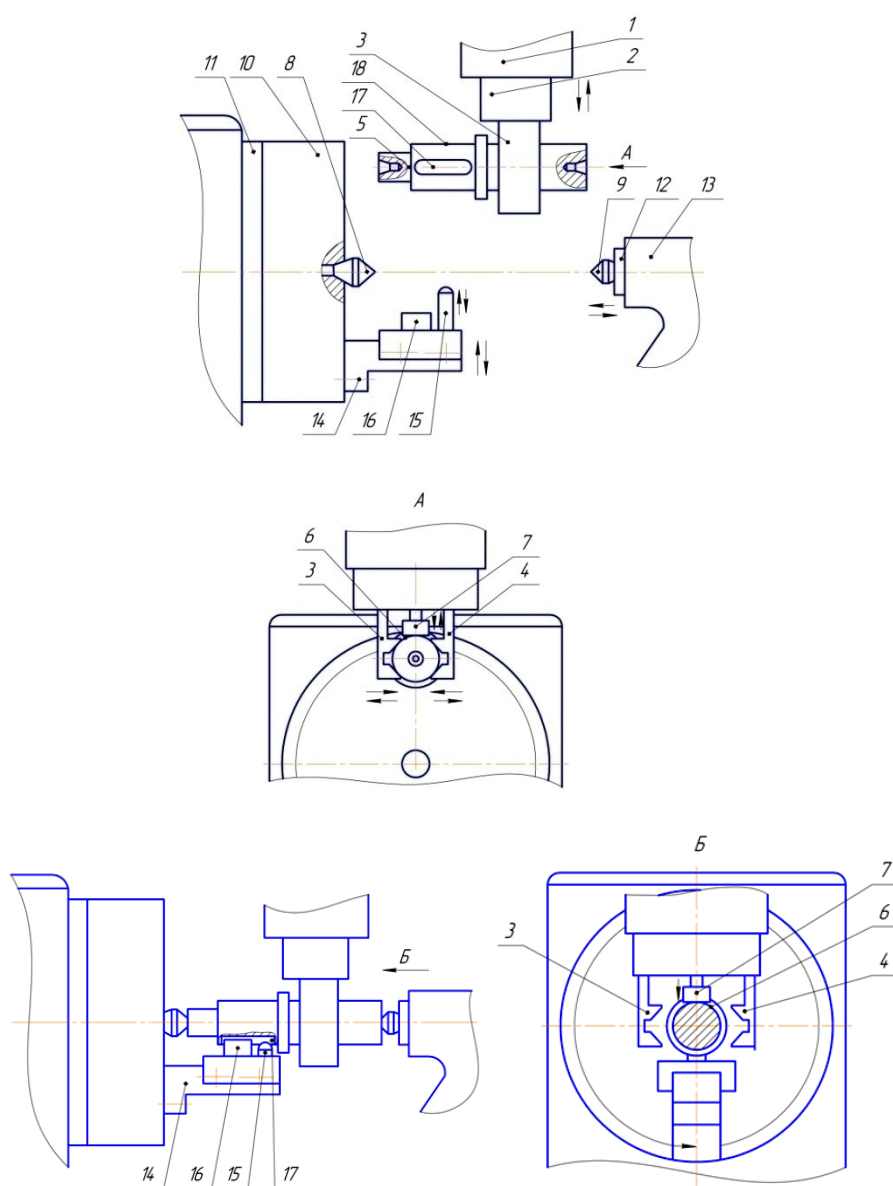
Схема способа установки вала со шпоночным пазом на центрах станка
